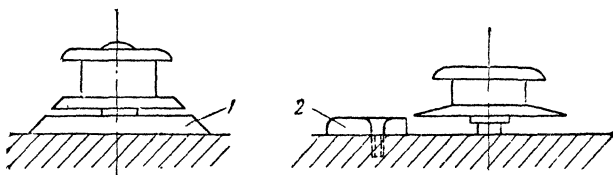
Два способа облегчения зарядки ленты на поворотный ролик: 1 — конусная шайба; 2 — направляющая планка
